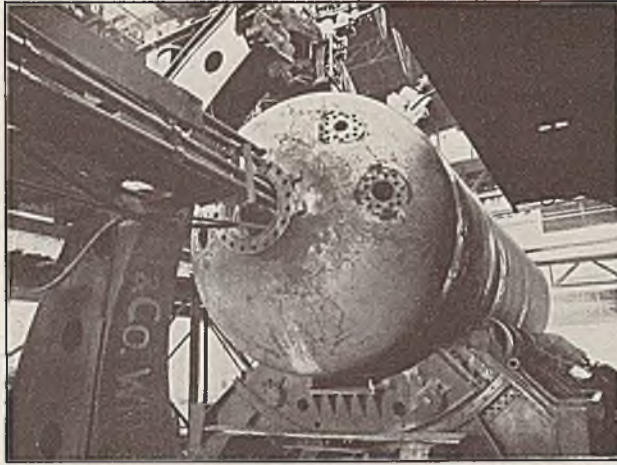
Elliptisch gewölbter Pintschboden zum Einschweißen 1700 mm Φ \times 26 mm mit 7 ausgepressten Löchern
